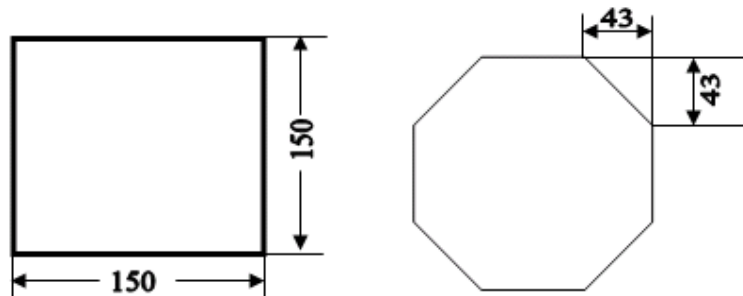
Découpage de la tôle en forme d'éprouvette
